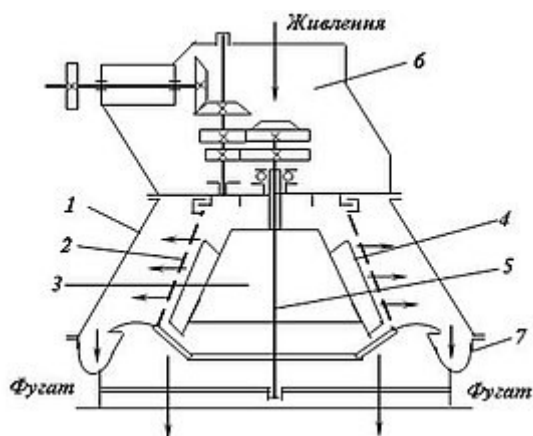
Центрифуга фільтруюча шнекового типу: 1 – корпус центрифуги; 2 – фільтруючий ротор; 3 – корпус шнека; 4 – шкребки; 5 – головний вал; 6 – завантажувальний циліндр; 7 – жолоб для фугату.
